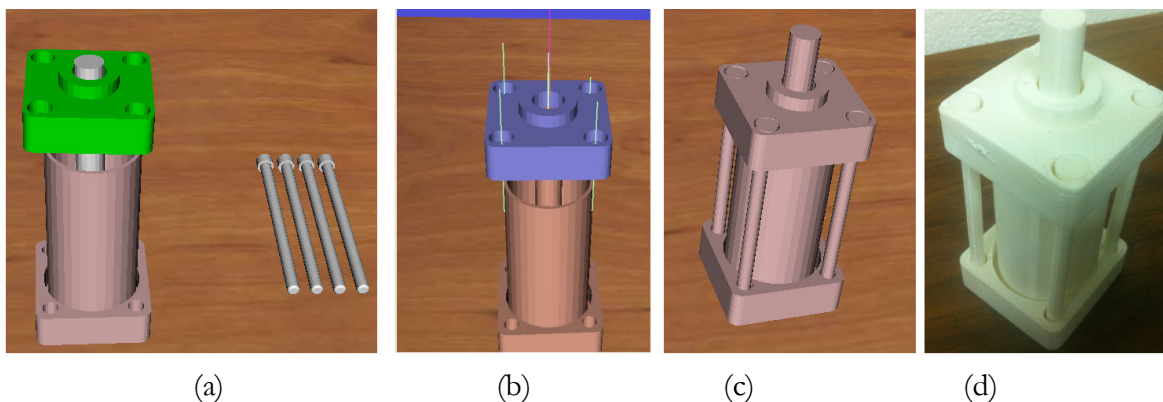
Ensamble de cilindro neumático: (a) ensamble utilizando únicamente PBM, (b) ensamble utilizando DACs, (c) ensamble final, (d) ensamble real.
